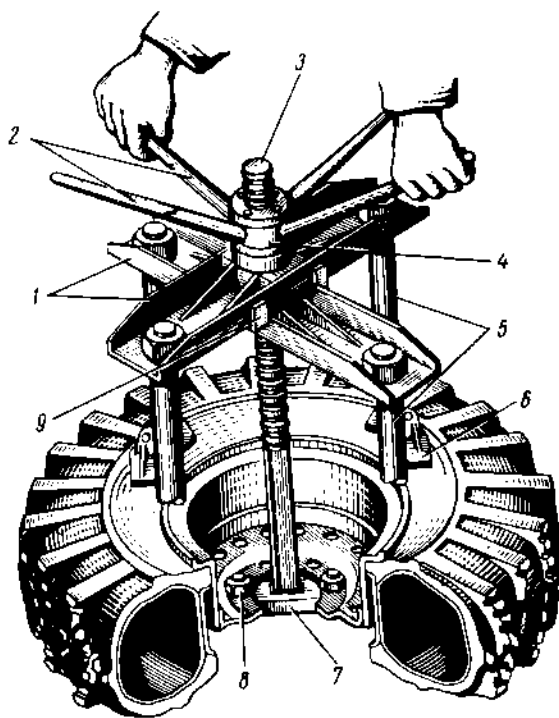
Снятие шины с обода колеса с помощью приспособления:
